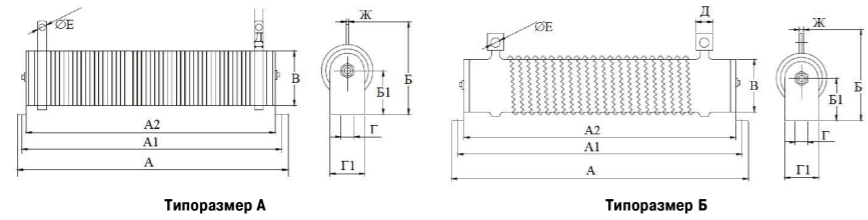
Габаритно-установочный чертеж резисторов серии РБ1
